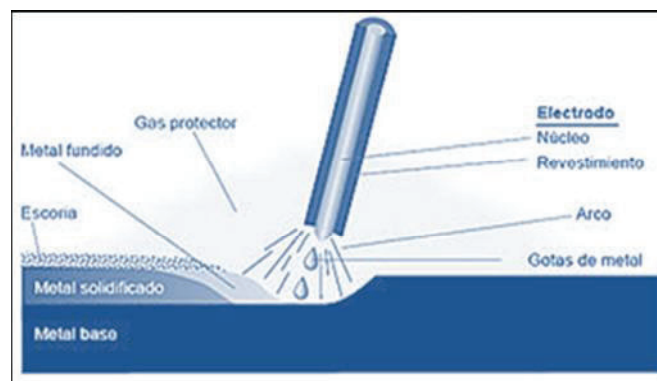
1 Elementos de un proceso de soldadura SMAW
